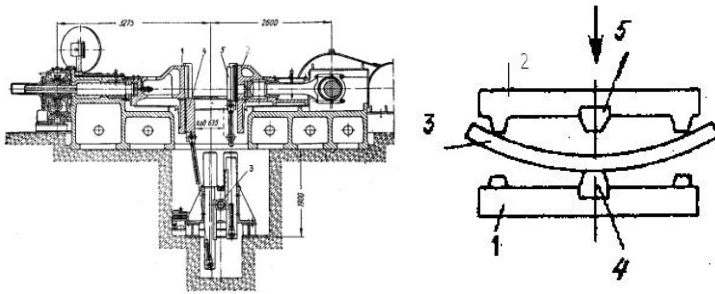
Горизонтальний прес для виправлення балок (а) та схема лабораторної установки (б).
